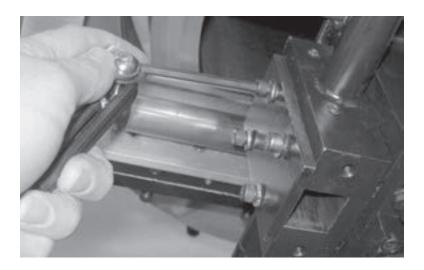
Desserrez les vis du plateau porte-outil pour monter le porte-outil sur la traverse.
